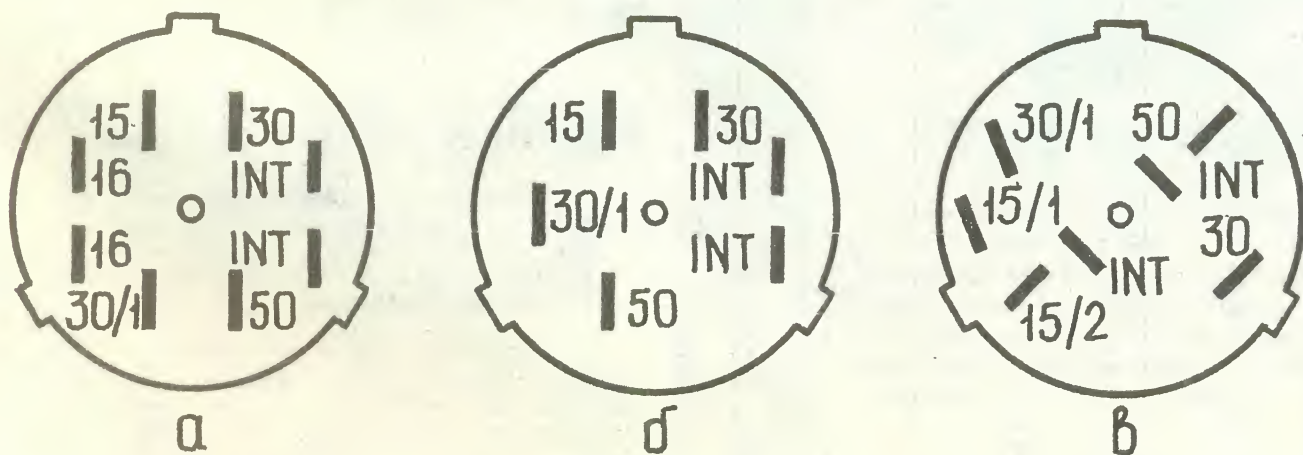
Расположение и маркировка выводов выключателей зажигания: а — ВК 347; б — 15.3704; в — 2105-3704100.
